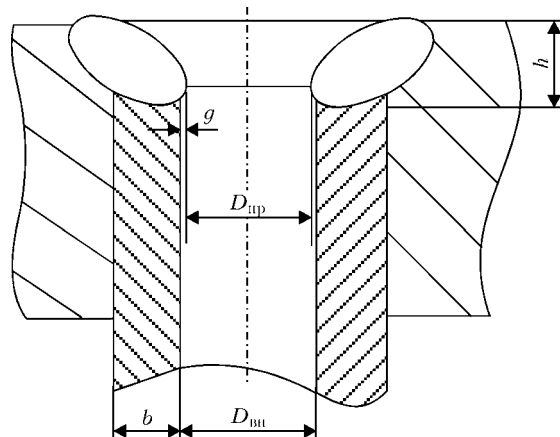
Схема сварного соединения труба-трубная решетка: h — высота рабочего сечения шва; g — величина наплыва шва; b — толщина стенки трубы; $D_{вн}$ — внутренний диаметр трубы; $D_{пр}$ — диаметр проходного сечения трубы
